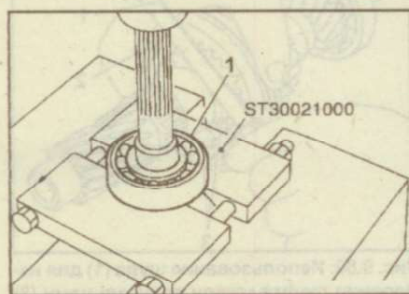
Выпрессовка первичного вала из переднего подшипника (1)
